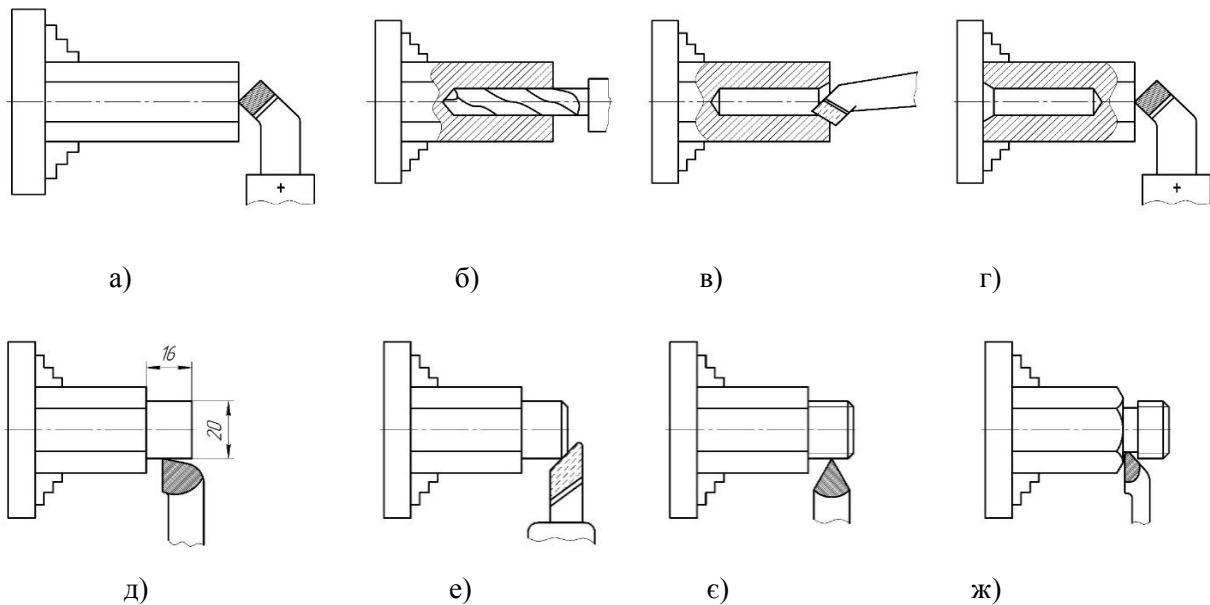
Етапи обробки поверхонь лівої різьбової частини штуцера
